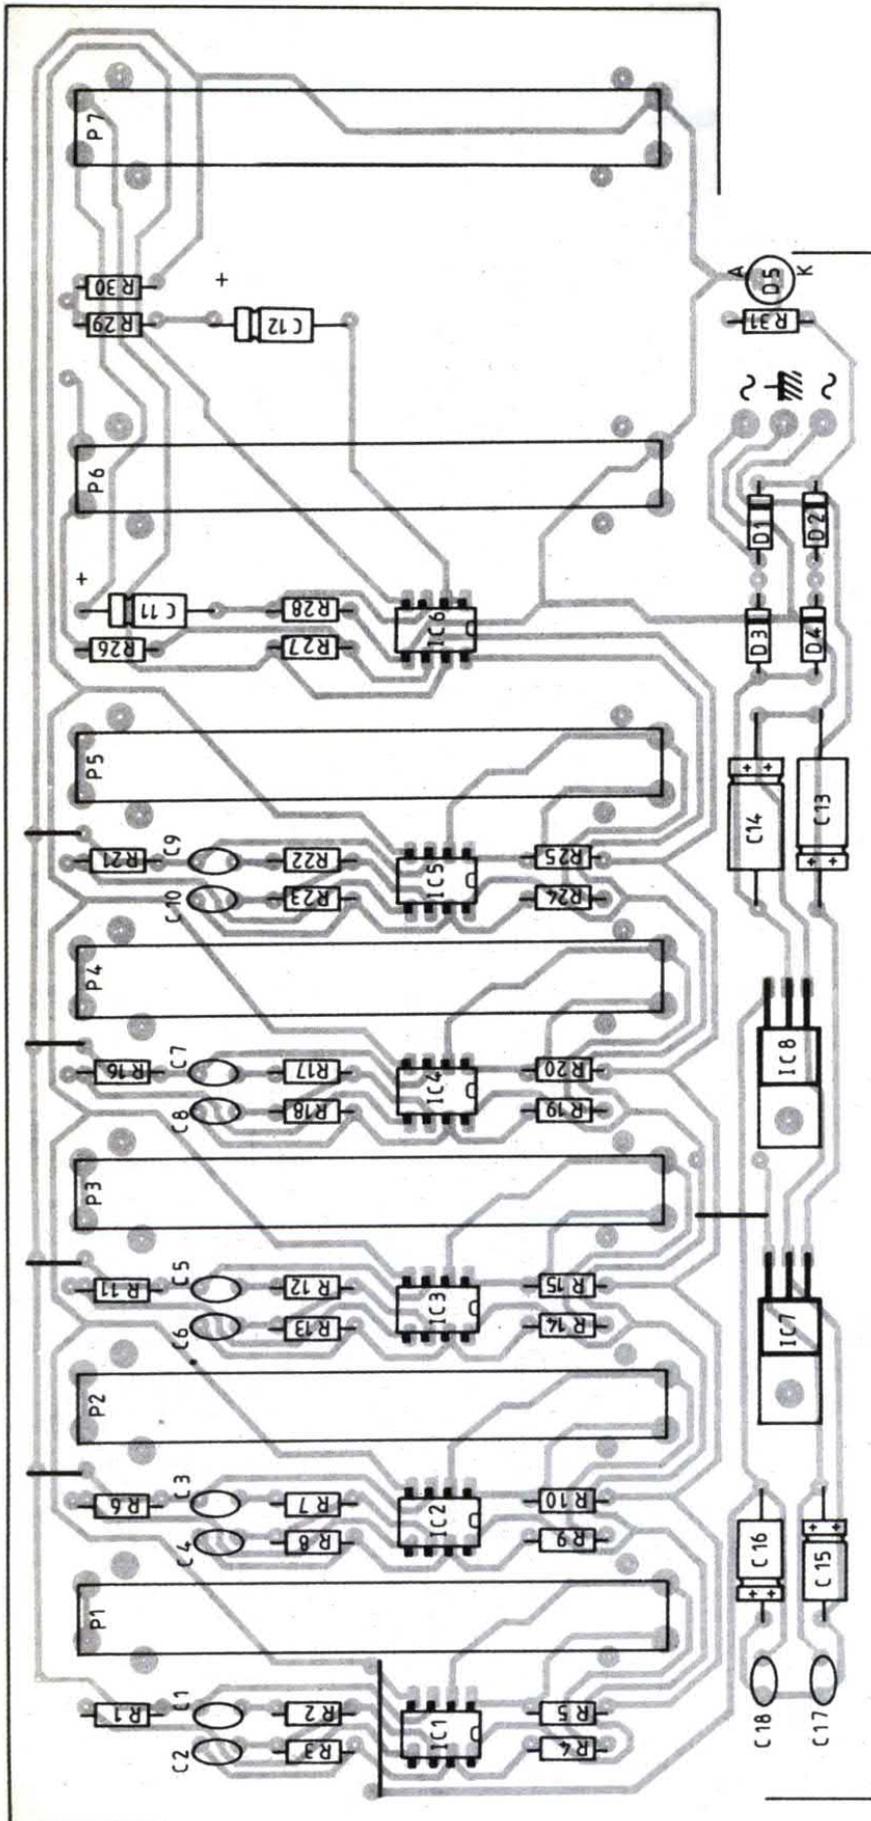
Disposizione dei componenti del banco di mixaggio: il circuito stampato raccoglie tutti i componenti, eccettuati il trasformatore ed il portafusibile.
